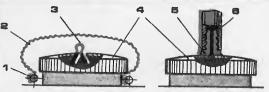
Защита дренажного отверстия пробки бака; 1 — резиновое кольцо или проволока; 2 — кусок ткани; 3 — шплинт; 4 — пробка; 5 — шту-цер; 6 — трубка.
